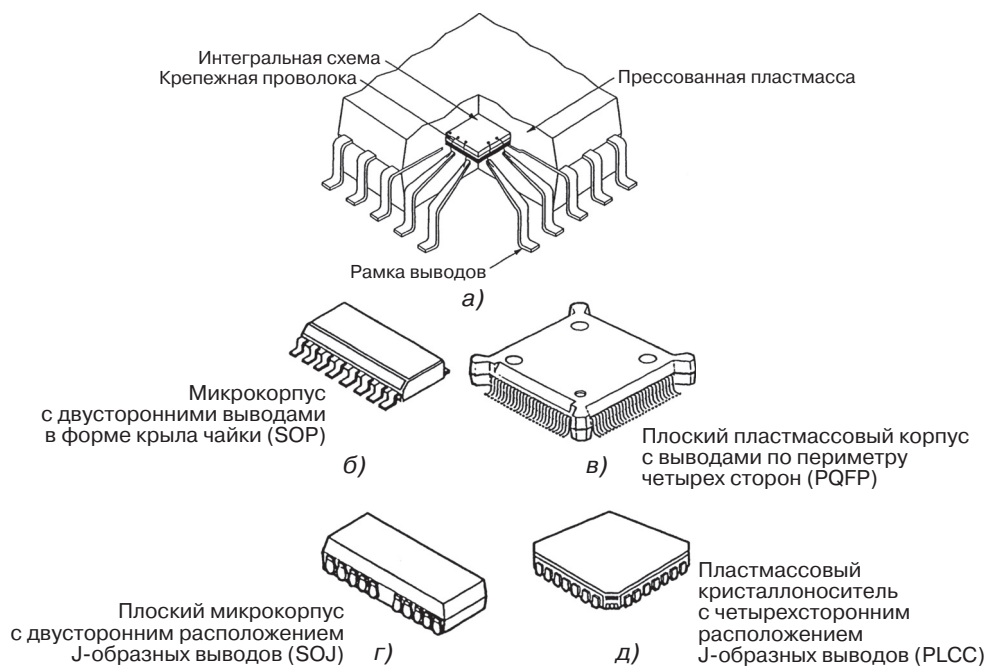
Типы пластмассовых корпусов для поверхностного монтажа
